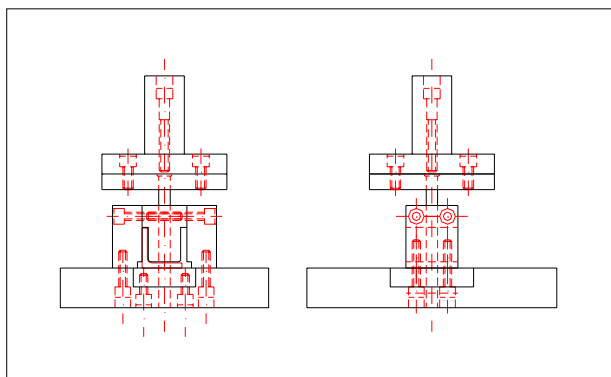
Desenho da ferramenta para furação da cantoneira de ligação
